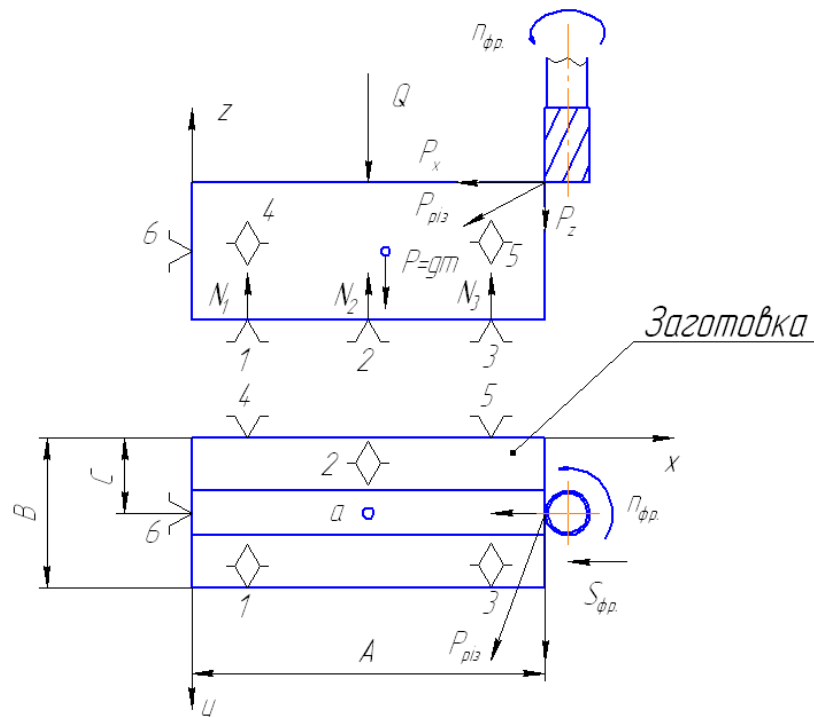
Схема установки заготовки з силами, що діють в процесі обробки
